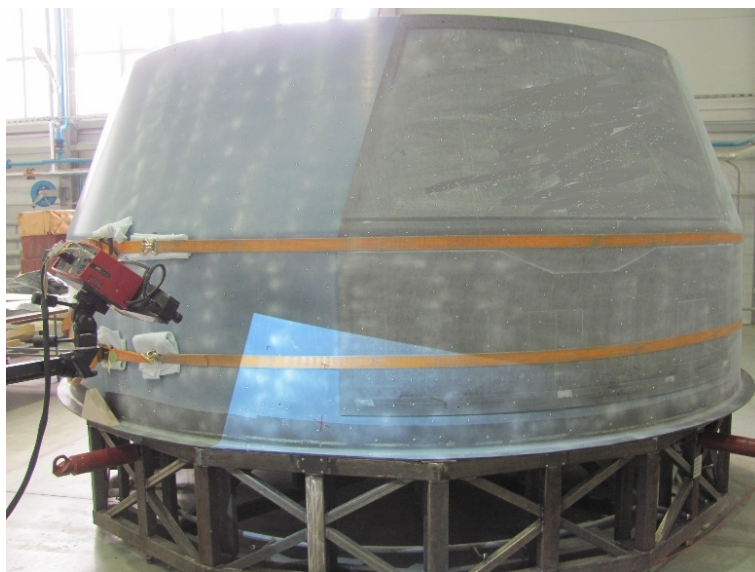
Оснастка корпуса переходного отсека в сборе
